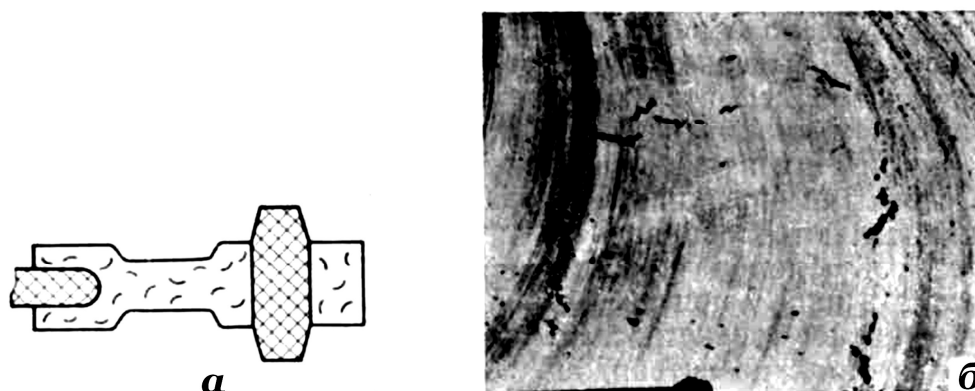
Азотные поры в отливке из модифицированного чугуна: а – схема; б – дефектная отливка
